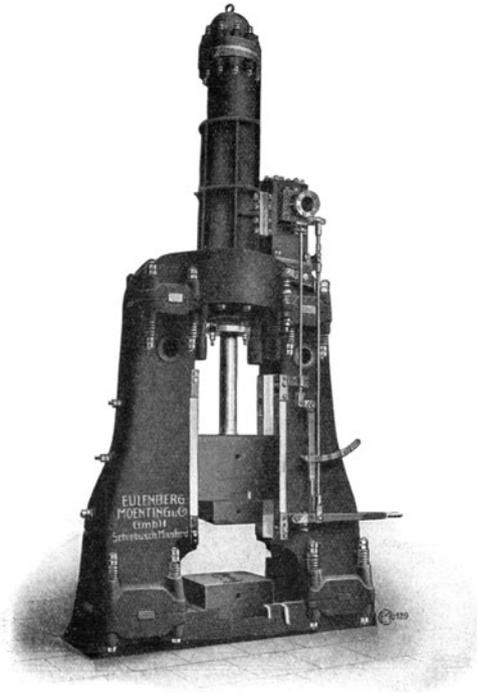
Dampfhammer von Eulenburg, Moening & Co. mit elastischer Verbindung des Zylinders und der Grundplatte mit den Ständern.
